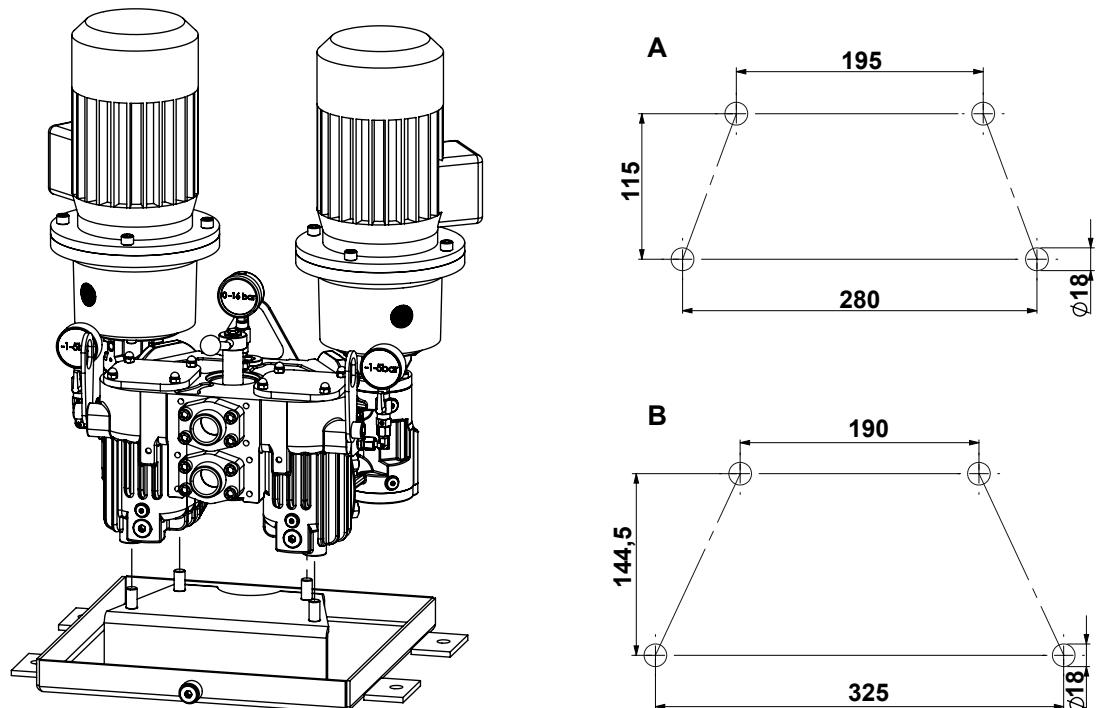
Montage auf Grundrahmen mit Ölwanne
